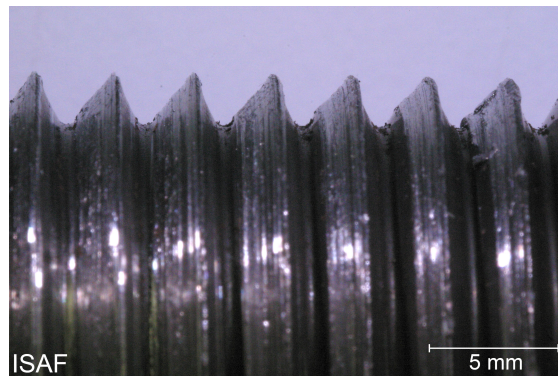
Gewindeprüfkörper axial belastet mit 180kN (Bolzen)
